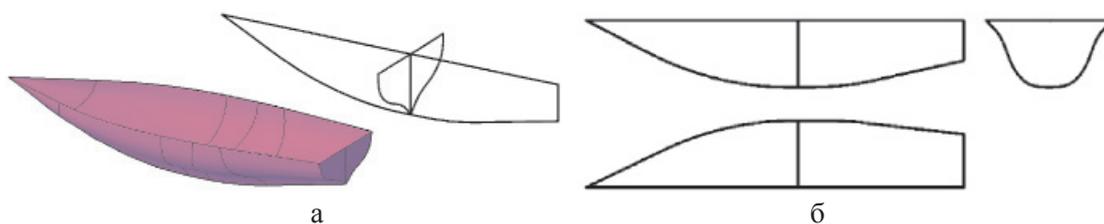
Трехмерная модель и плоский чертеж корпуса лодки
